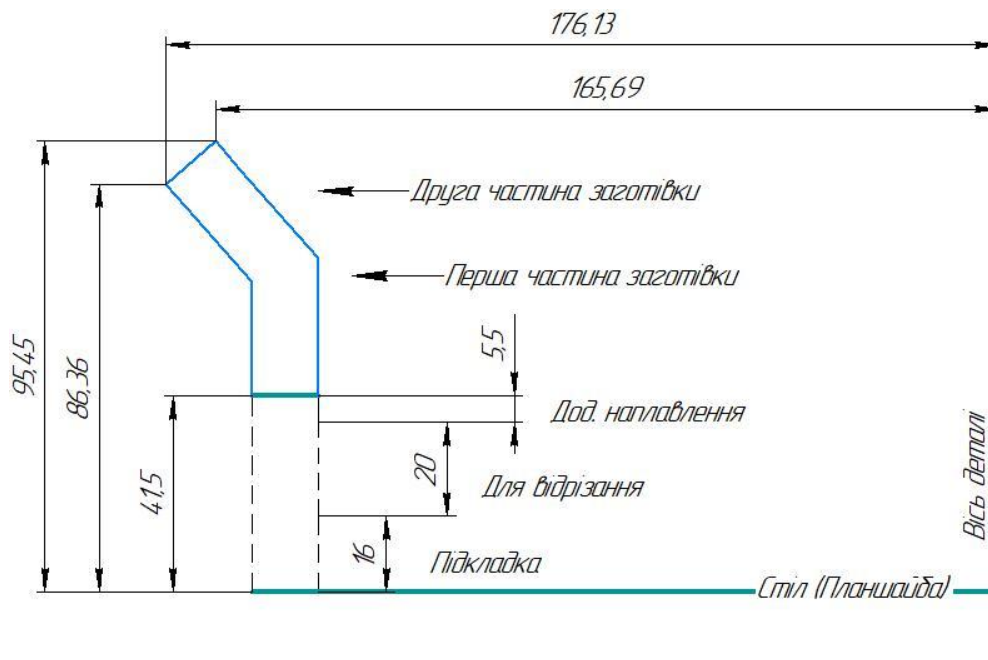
Креслення другої частини заготівлі 4500301001 (Зроблено в КОМПАС-3D v17)
